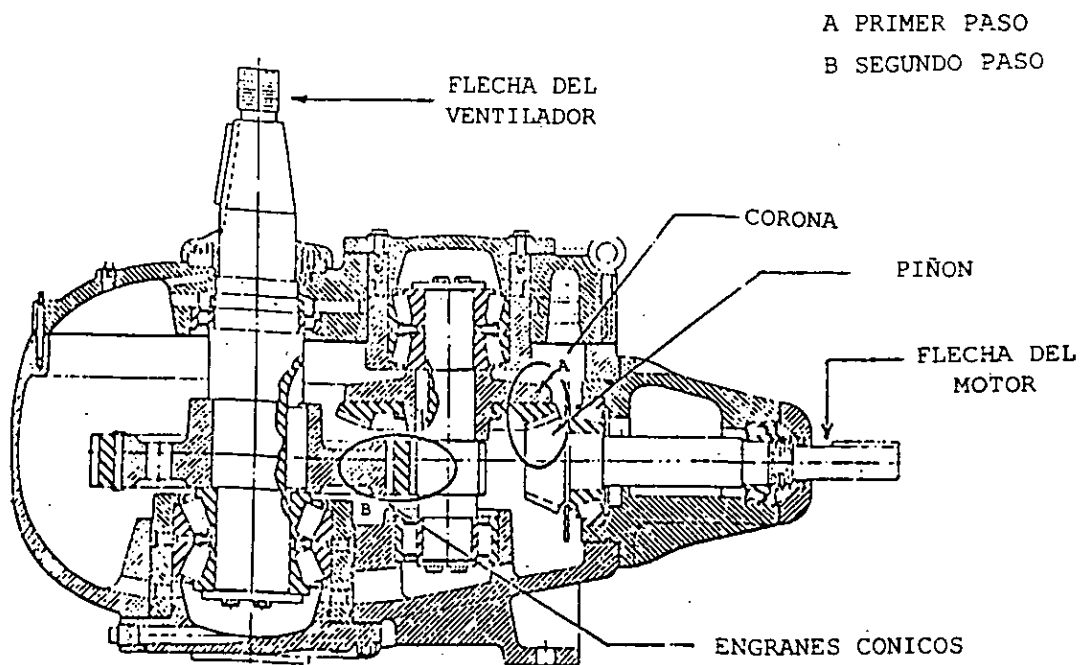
CORTE DEL REDUCTOR DE ENGRANES.
